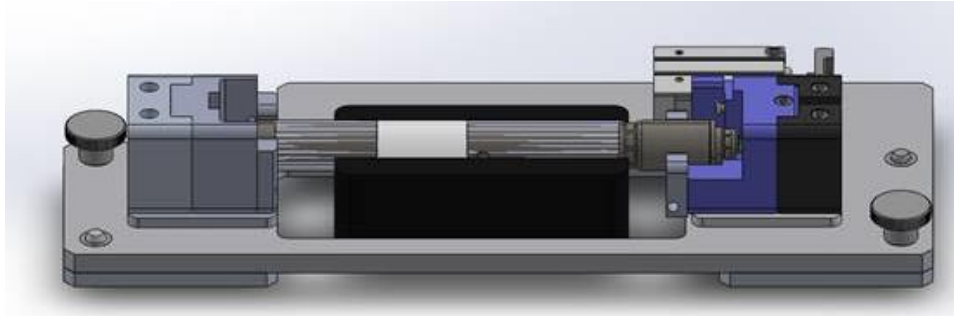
Fixture de chequeo de peso y continuidad en solidworks
